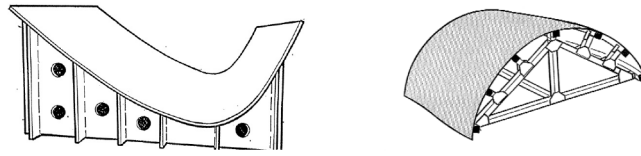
Hinterbaukonstruktionen: geschlossene Plattenkonstruktion und Fachwerk [4]
